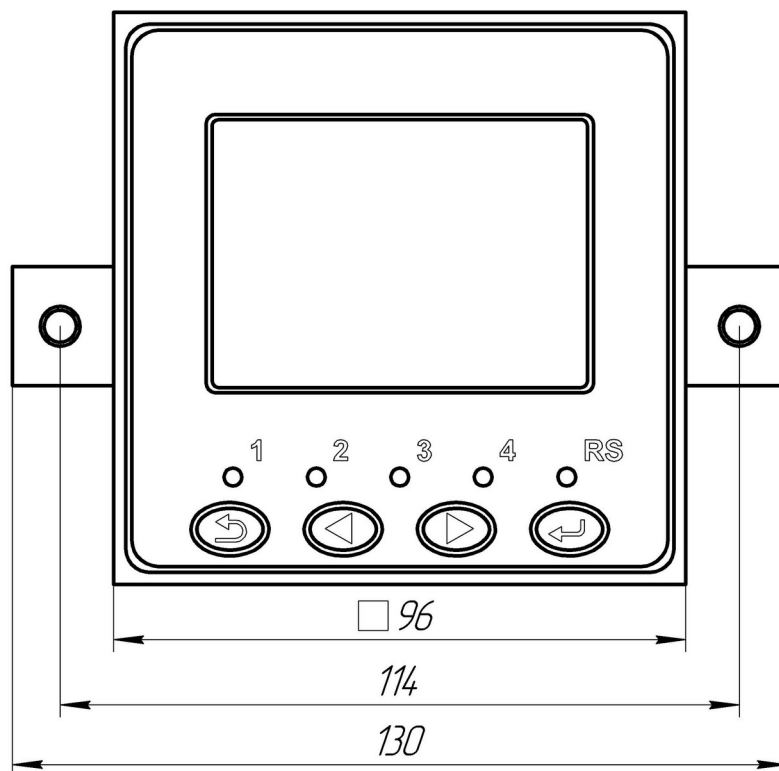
Габаритные размеры контроллера щитового исполнения
